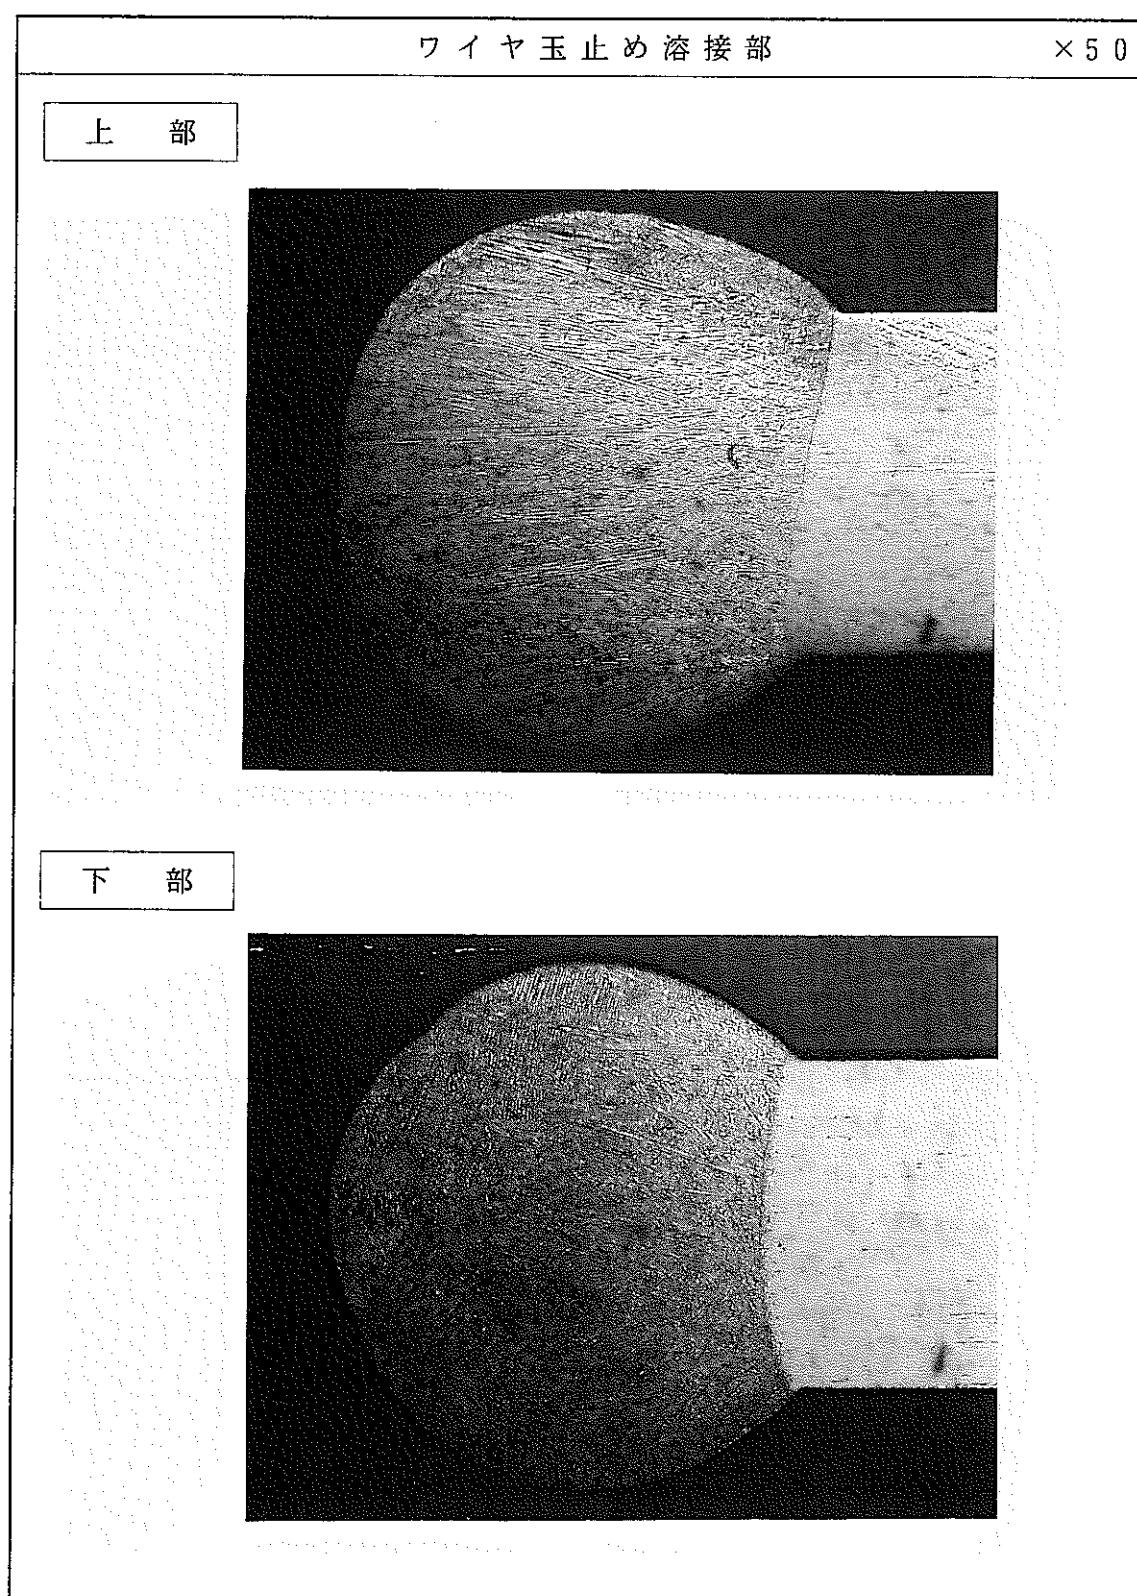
断面金相（ワイヤ玉止め溶接部）
